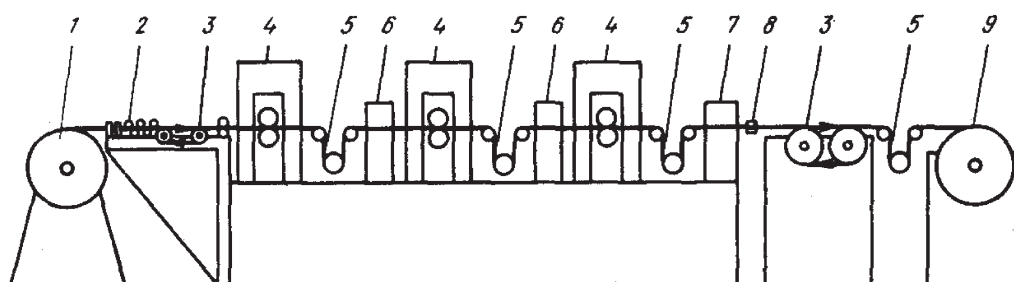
Схема плющильного стана: 1 – размоточное устройство; 2 – рихтовка; 3 – кабестан; 4 – клеть; 5 – датчик положения; 6 – клеть с вертикальными валками; 7 – калибровочная клеть; 8 – летучий микрометр; 9 – намоточное устройство
